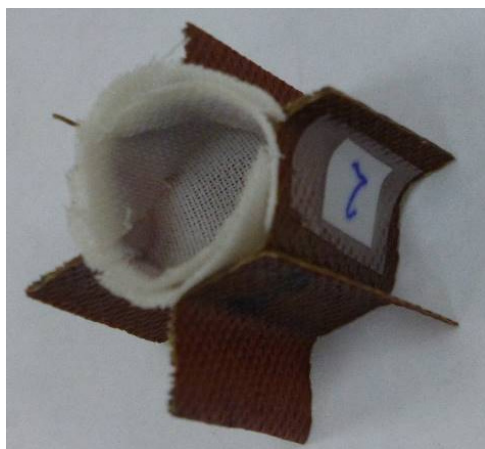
Образец сотового наполнителя с мембранной крышкой
